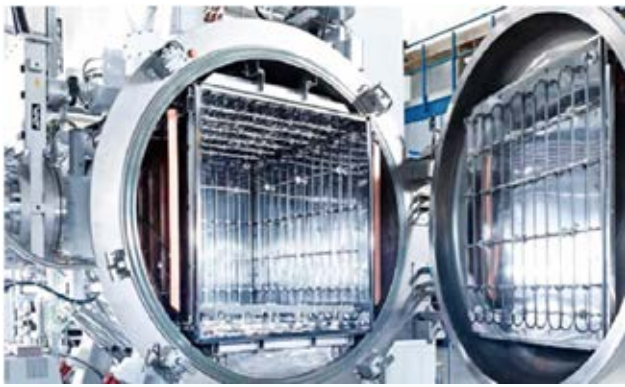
：來自德國的先進擴散焊接爐 / 採用真空擴散焊接技術加工內部帶隨行水路零件
